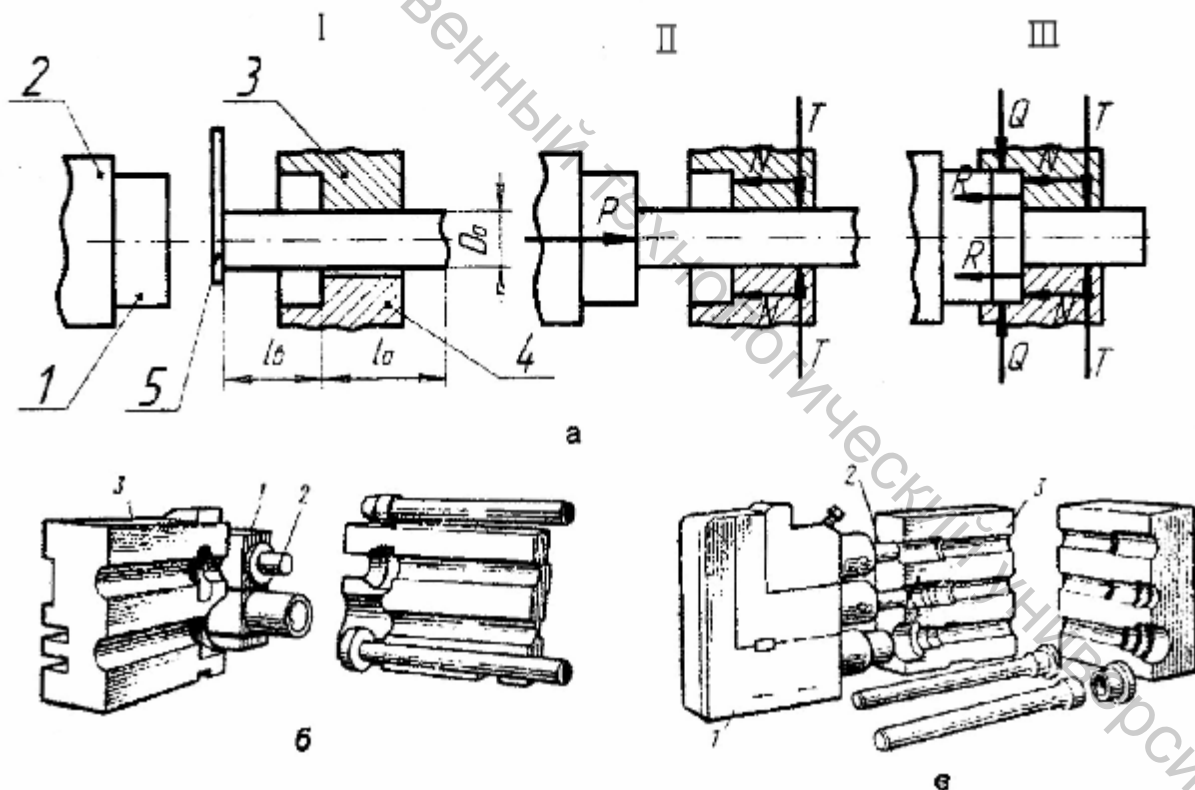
Штамповка на ГКМ: а - схема процесса штамповки, б - двухручьевого штамп, в - трехручьевого штамп. 1 - пуансон, 2 - блок пуансонов, 3 - матрица неподвижная, 4 - матрица подвижная, 5 - упор
